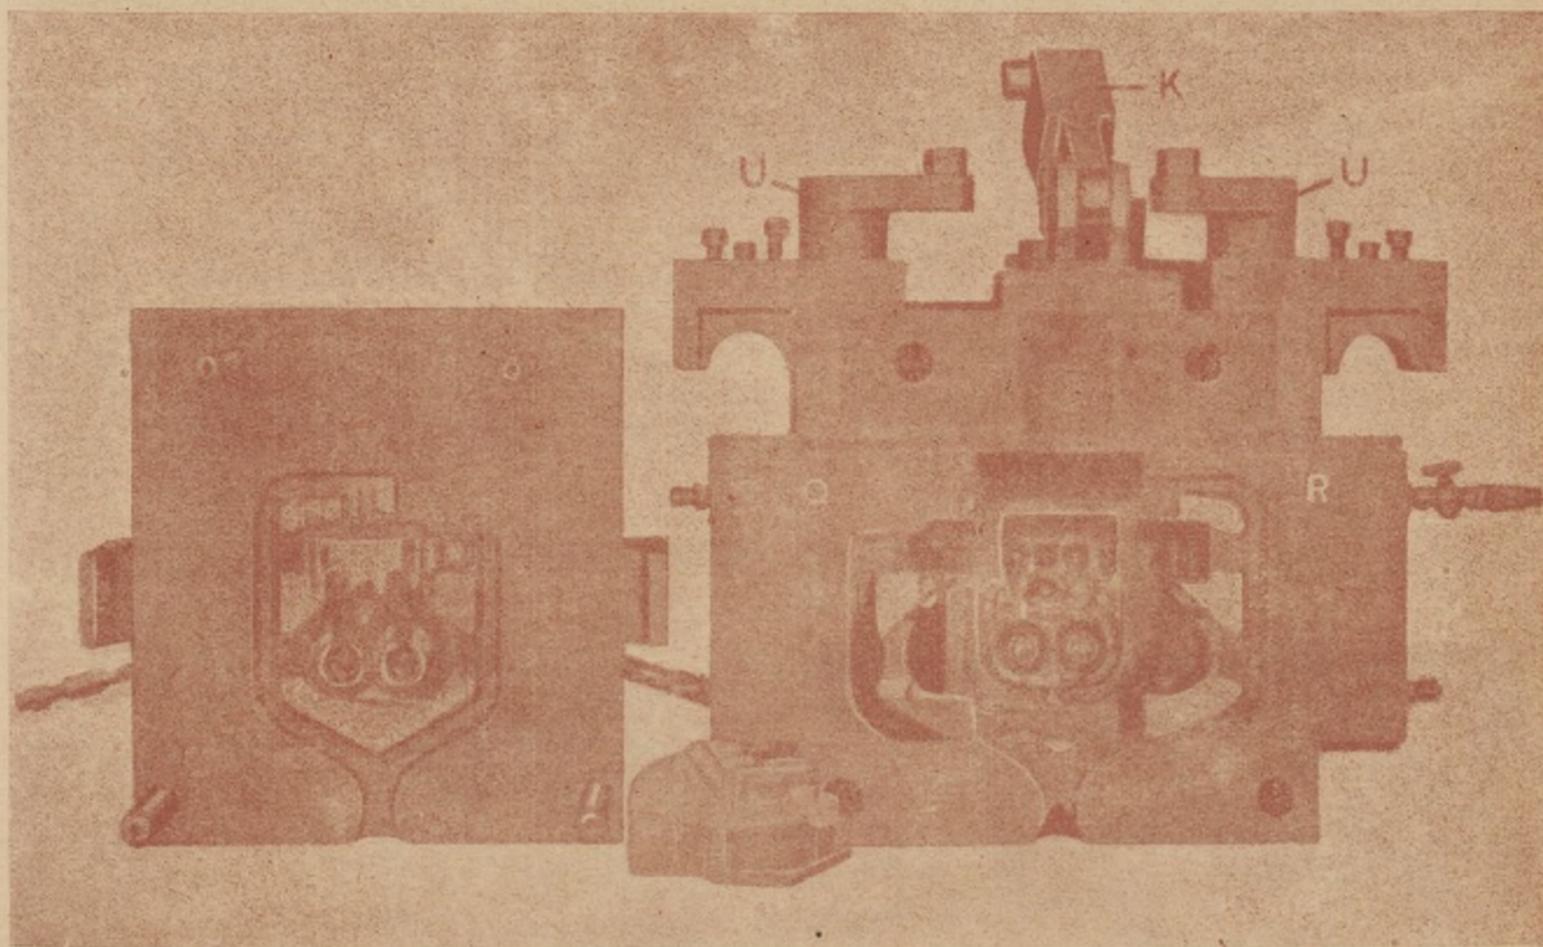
Coquilla para pieza de carburado. La parte fija está a la izquierda y la parte móvil a la derecha, está representada en posición cerrada, dispuesta para colada.
